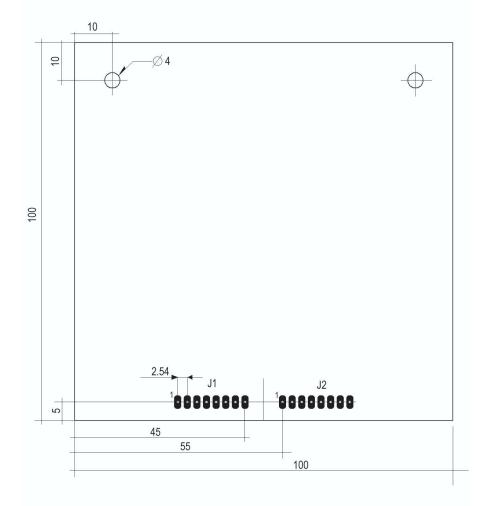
Le dimensioni (in millimetri) e la struttura di una singola scheda
